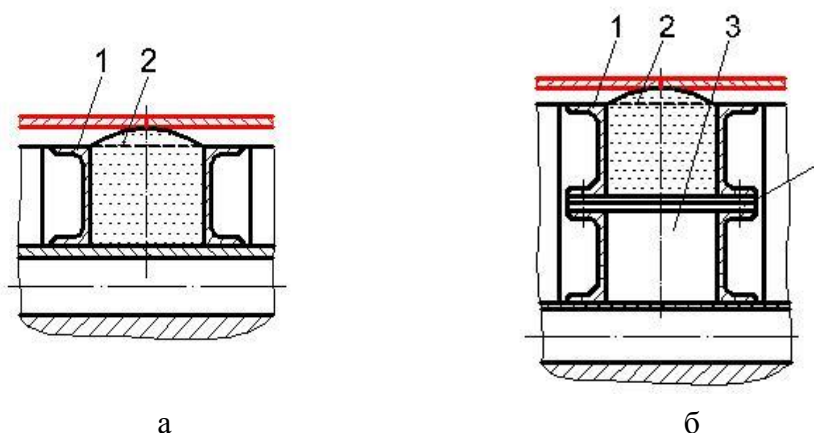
Основные типы стационарных флюсовых подушек для сварки прямолинейных стыковых соединений листовых полотнищ:
